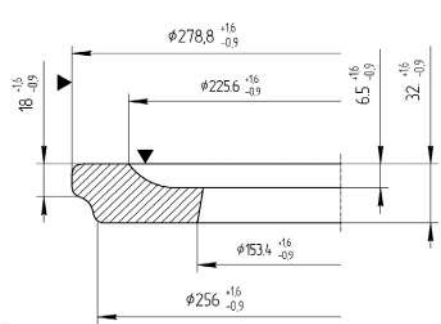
Ескіз заготовки у закритих штампах на КГШП
